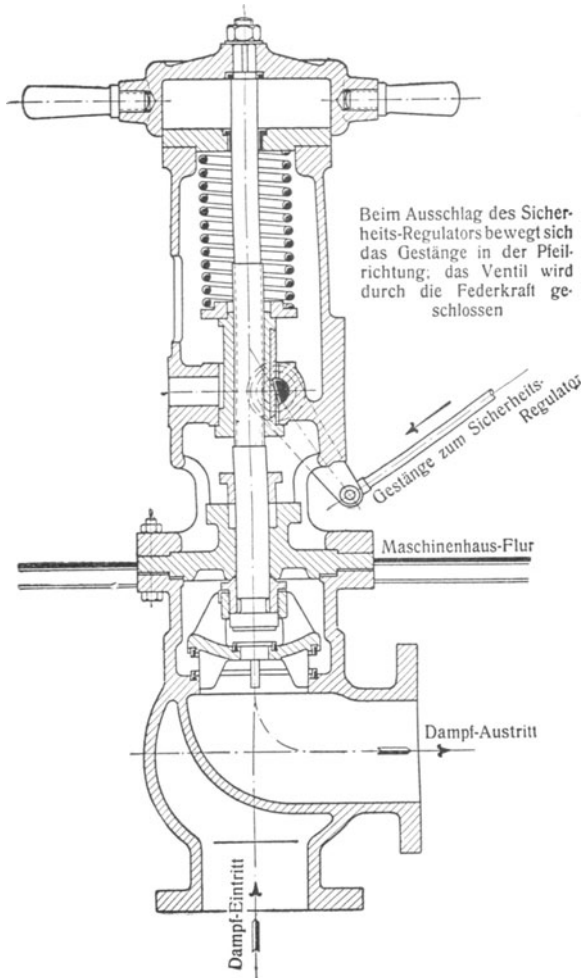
Selbstschlußvorrichtung der A.C.G.-Turbine.
